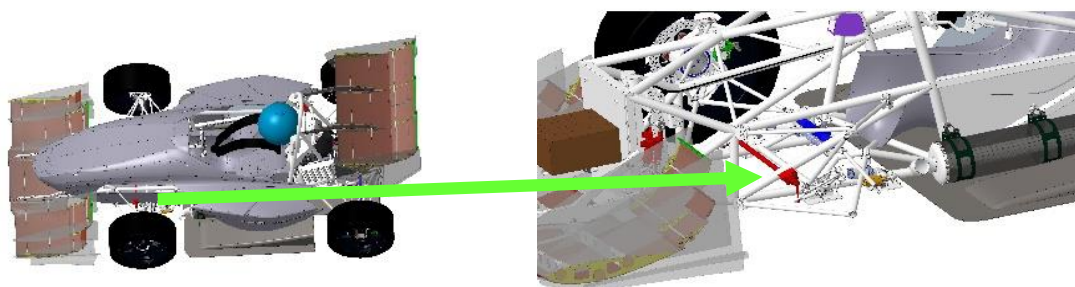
27 Druhá varianta uložení sestavy předního stabilizátoru
